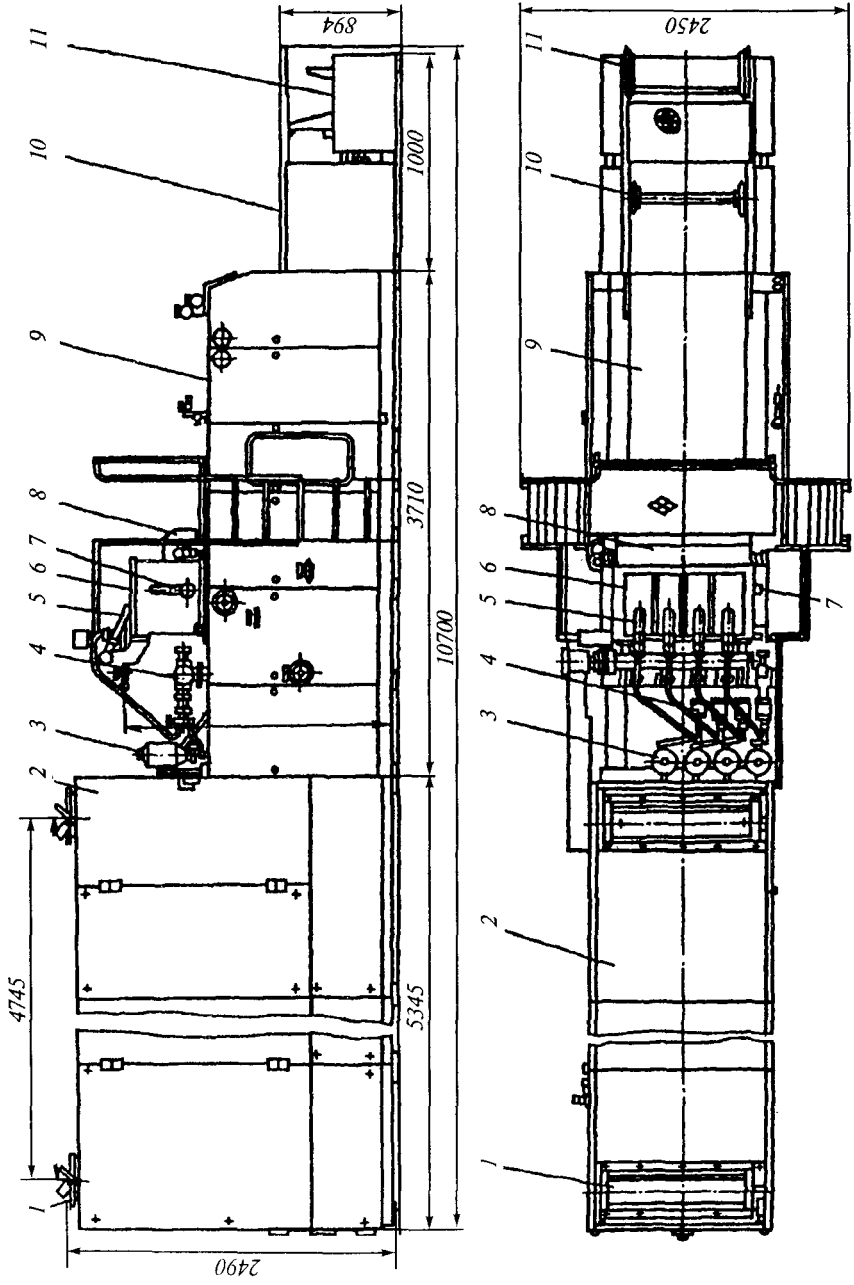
Мармеладогливочный агрегат ШФ1-М6
